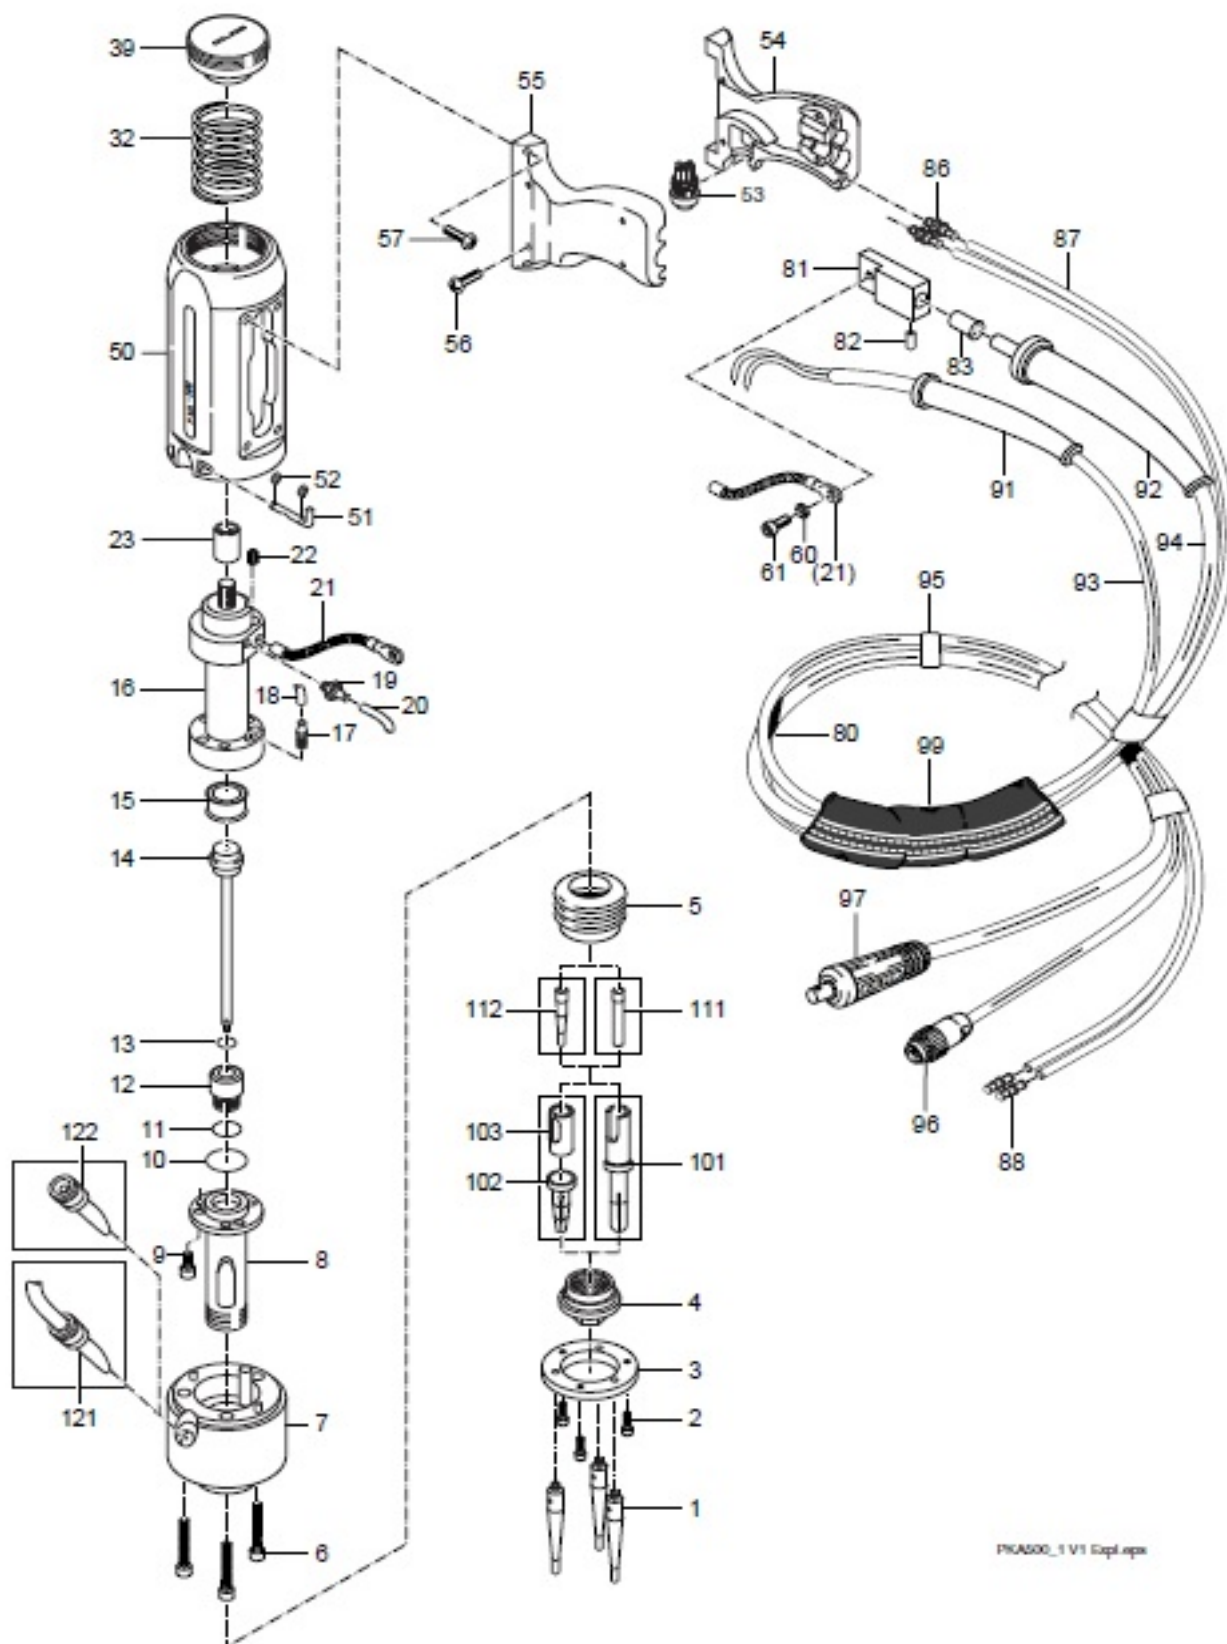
20 Explosionszeichnung Kontakt-Bolzenschweißpistole PKA-500
